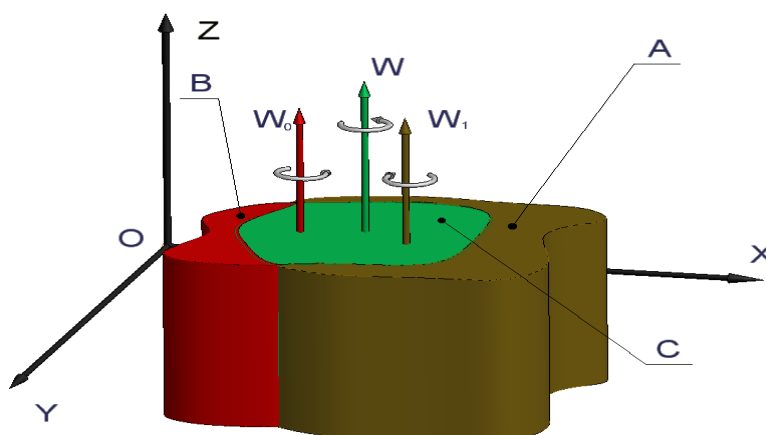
Общая модель формирования профиля зуба крупномодульного зубчатого колеса при механической обработке:
